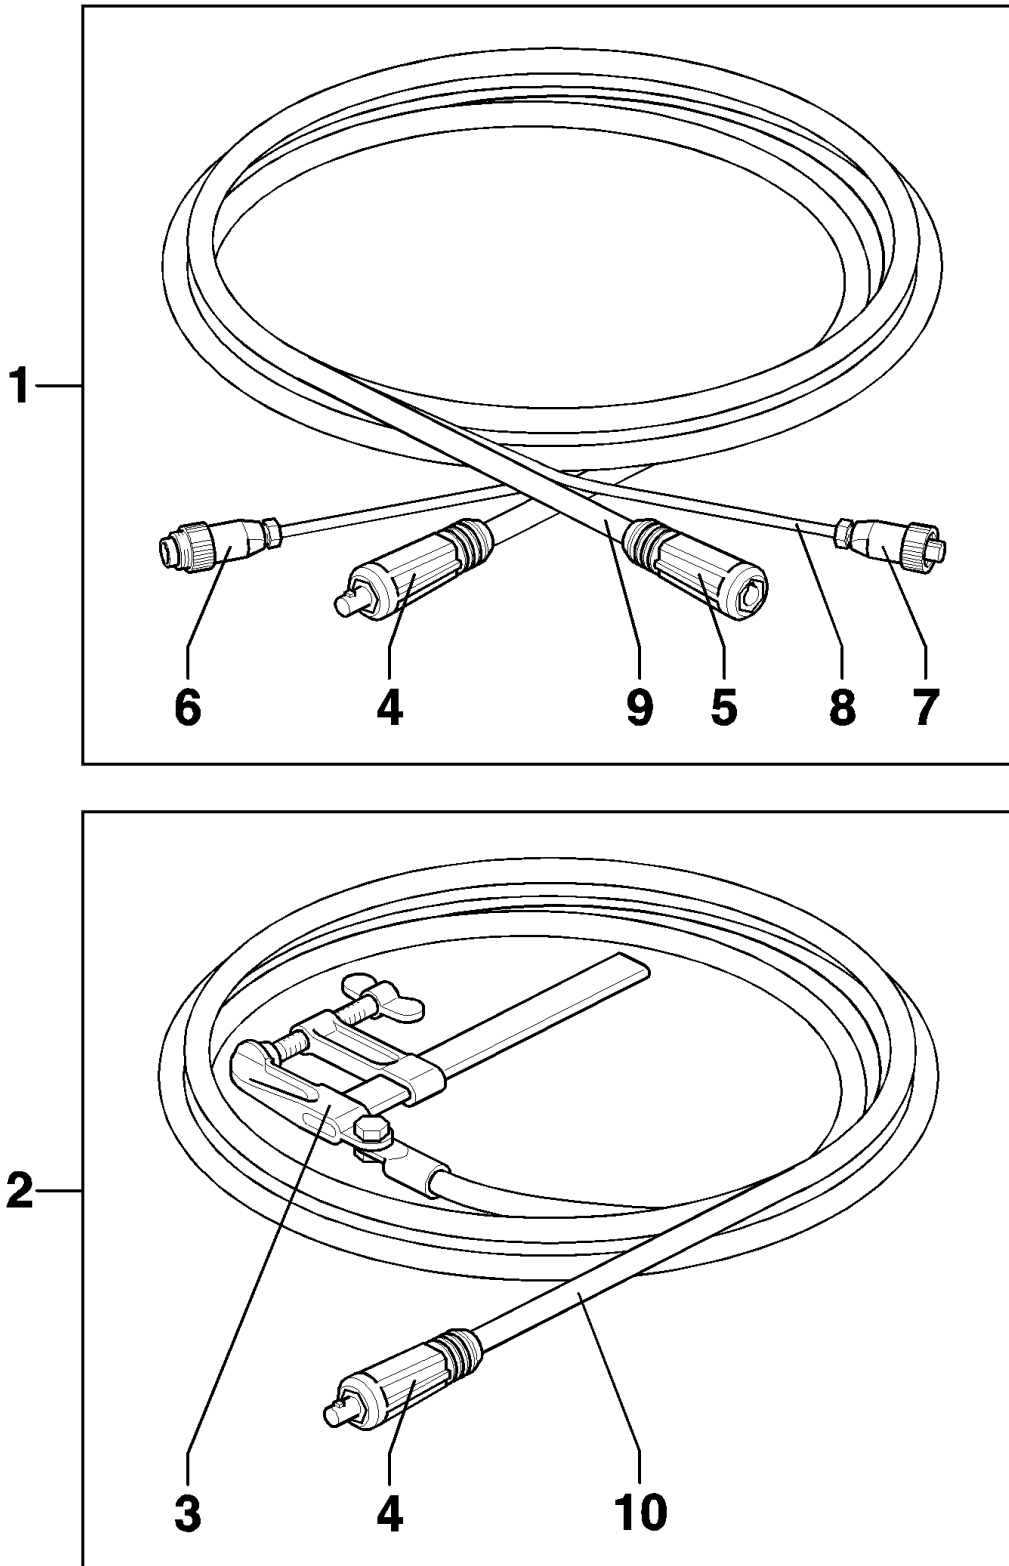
Schweißkabelverlängerung und Massekabel
